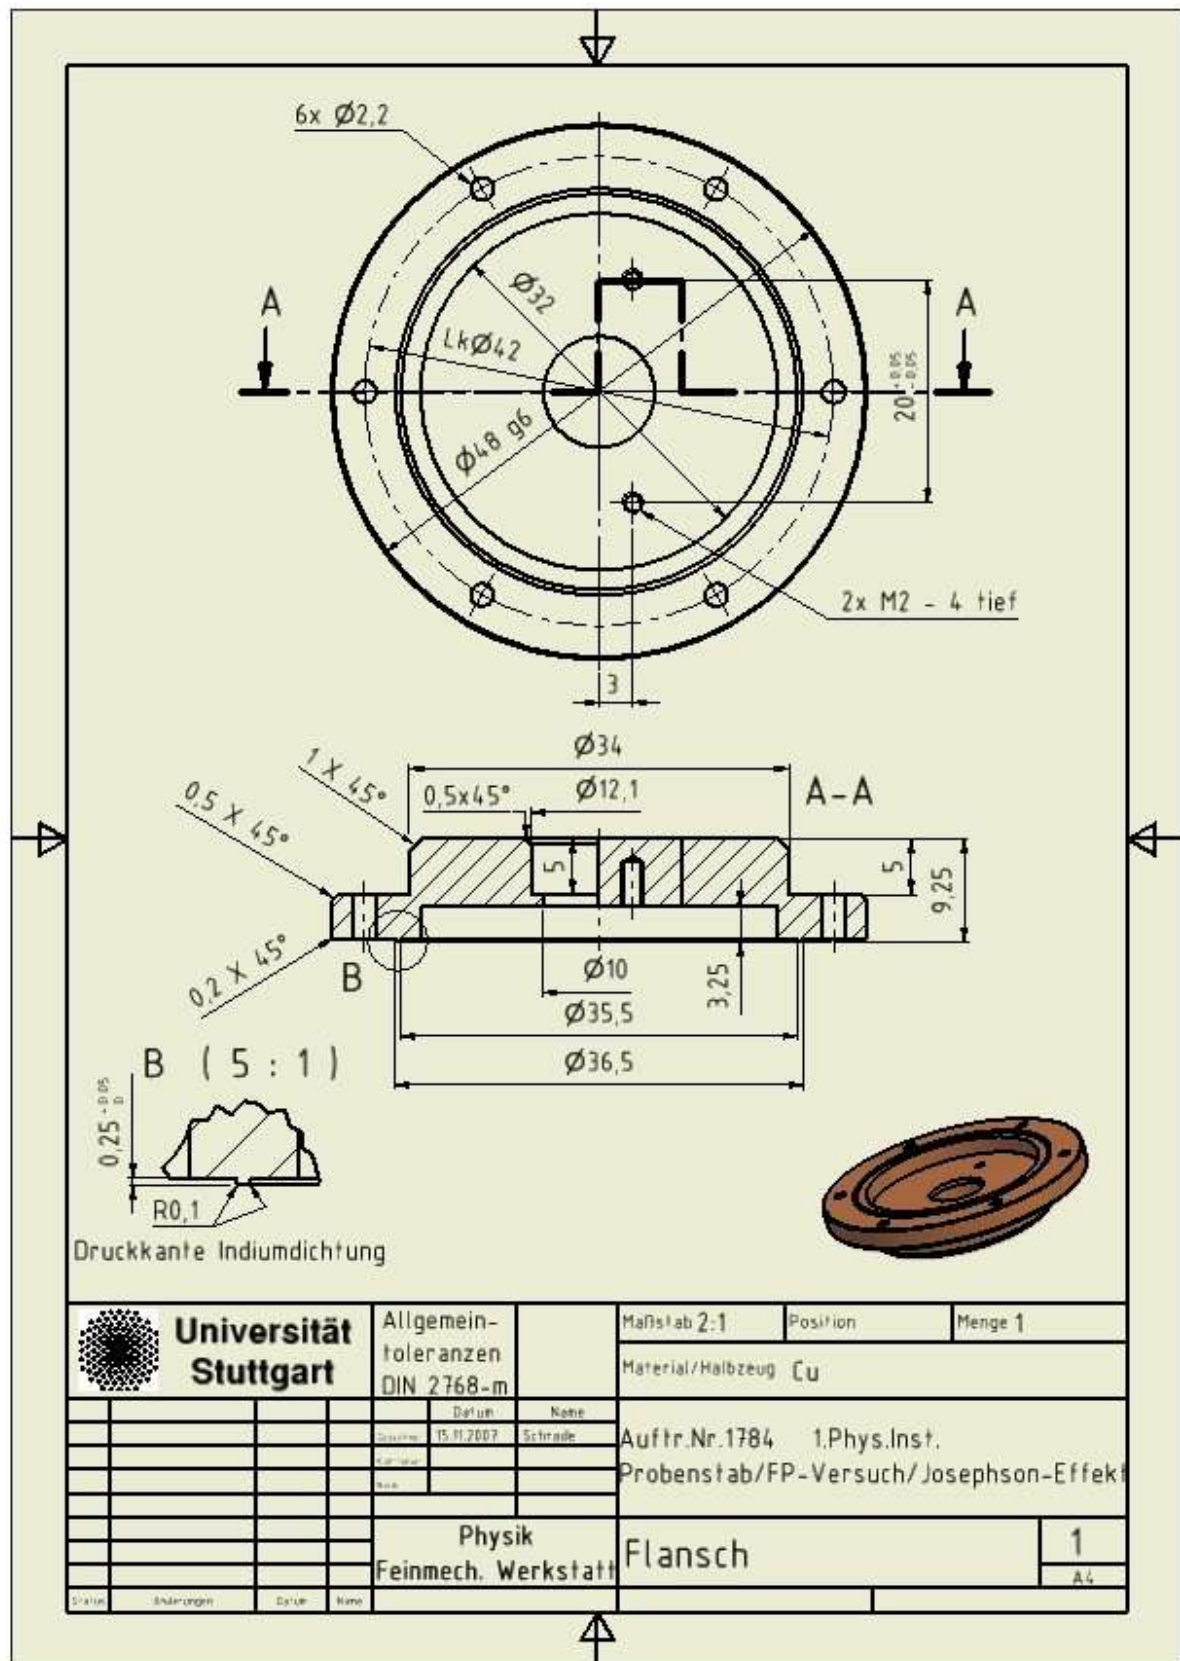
Technische Zeichnung für den Kupferflansch.
